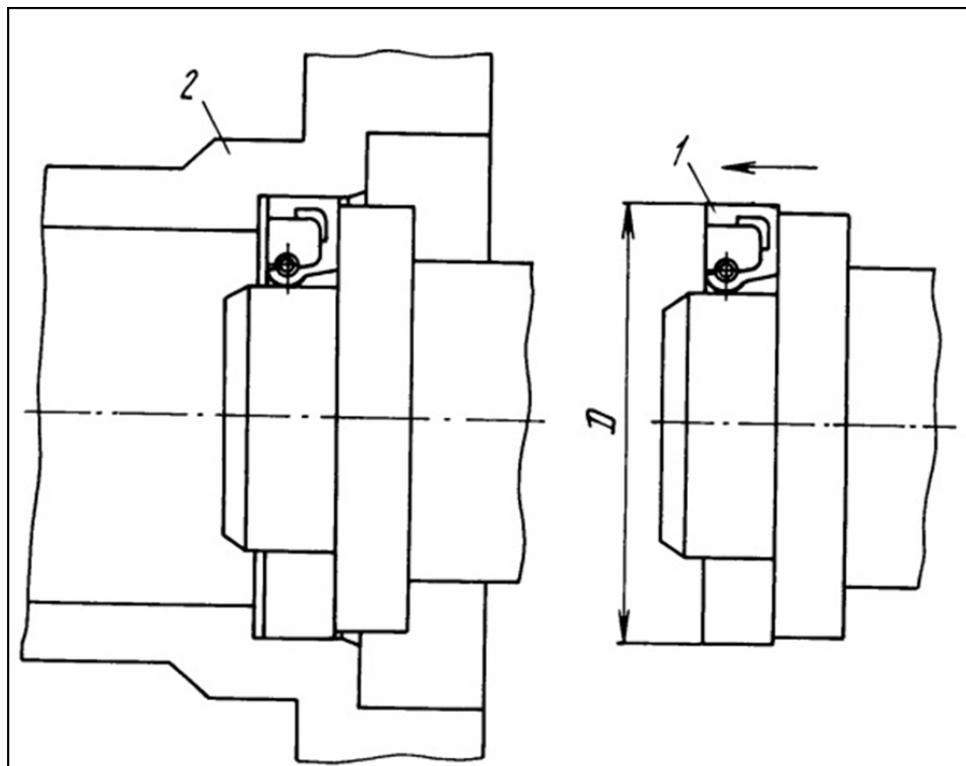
Запрессовка манжеты в базовую деталь
